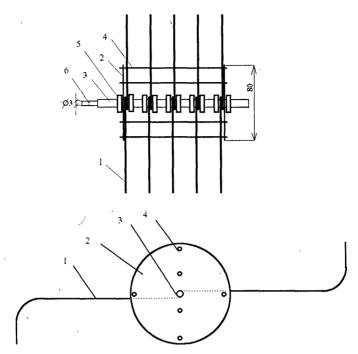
Барабан сброса и подъема грузила: 1 — спица; 2 — щечки; 3 — вал; 4 — распорки; 5 — гайки; 6 — отверстие под шплинт
